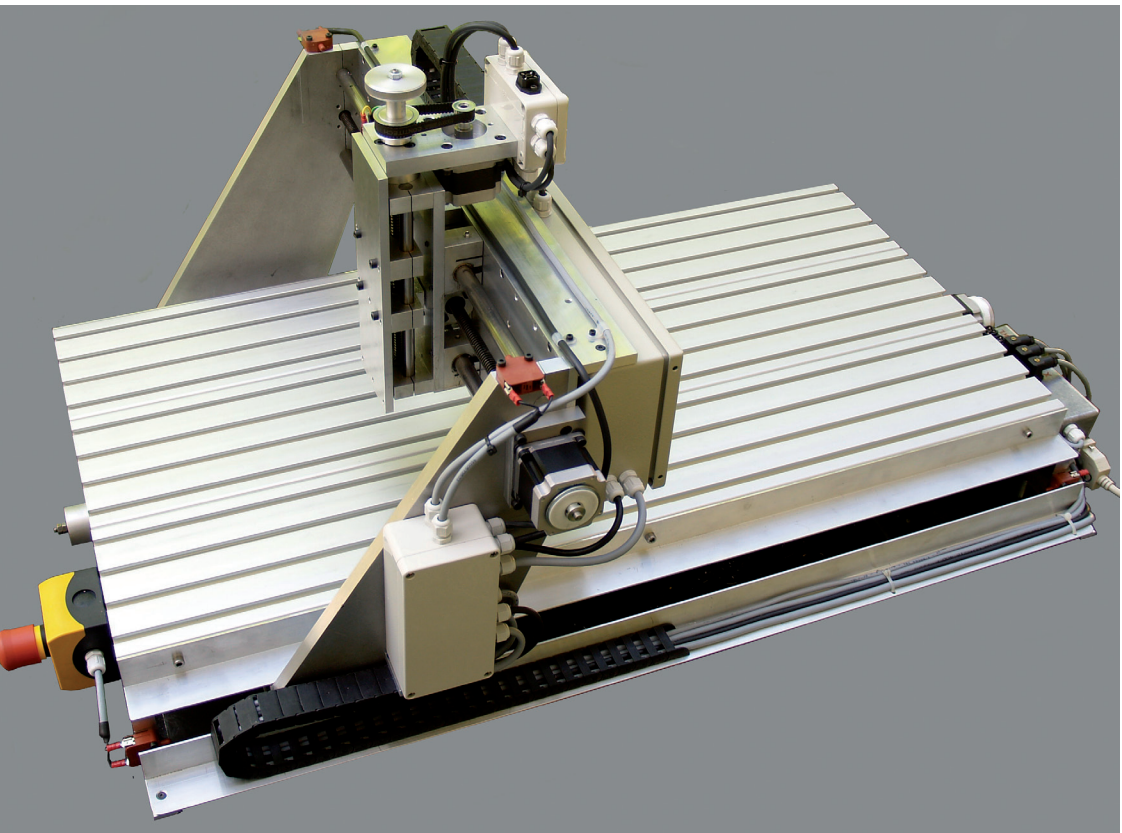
Meine erste, selbstgebaute Portalfräsmaschine, es fehlt noch der Fräsmotor
